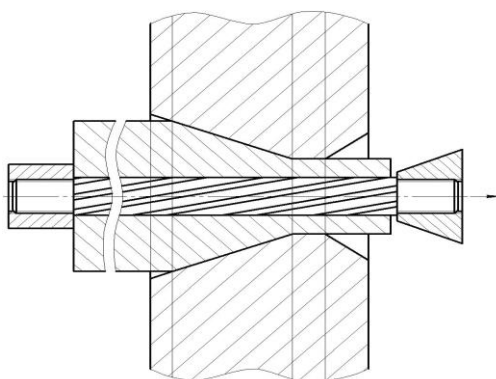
Схема обжатия ствольной заготовки в конической матрице
